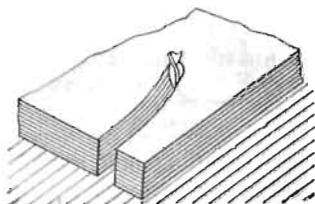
Схема фрезерования пакета листов пальцевой фрезой
